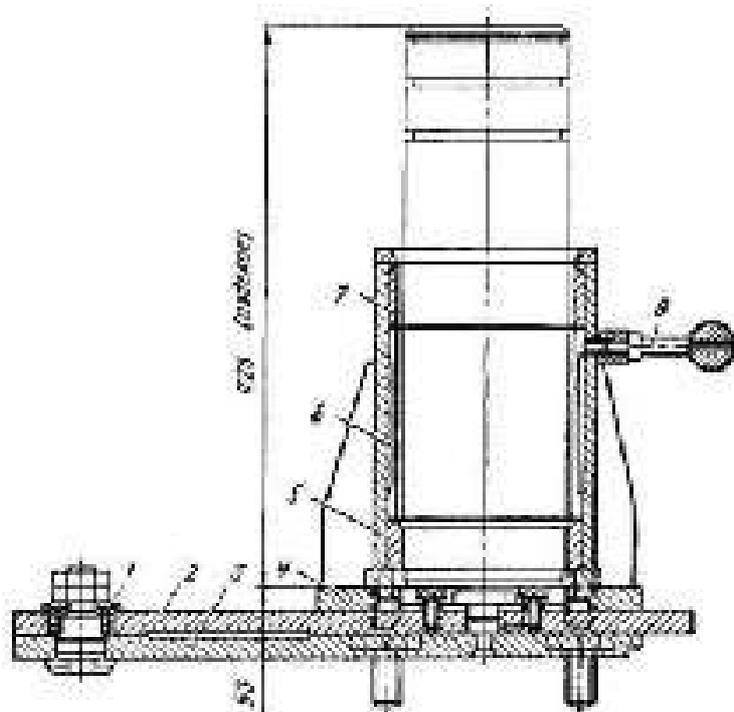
Припособление для сборки телескопического подъемника
